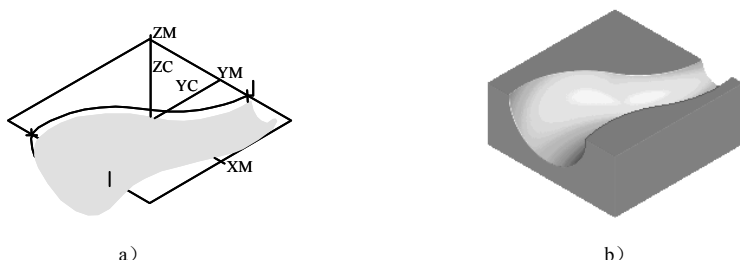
固定轴曲面轮廓铣精加工的“切削刀具路径”和“切削验证”
